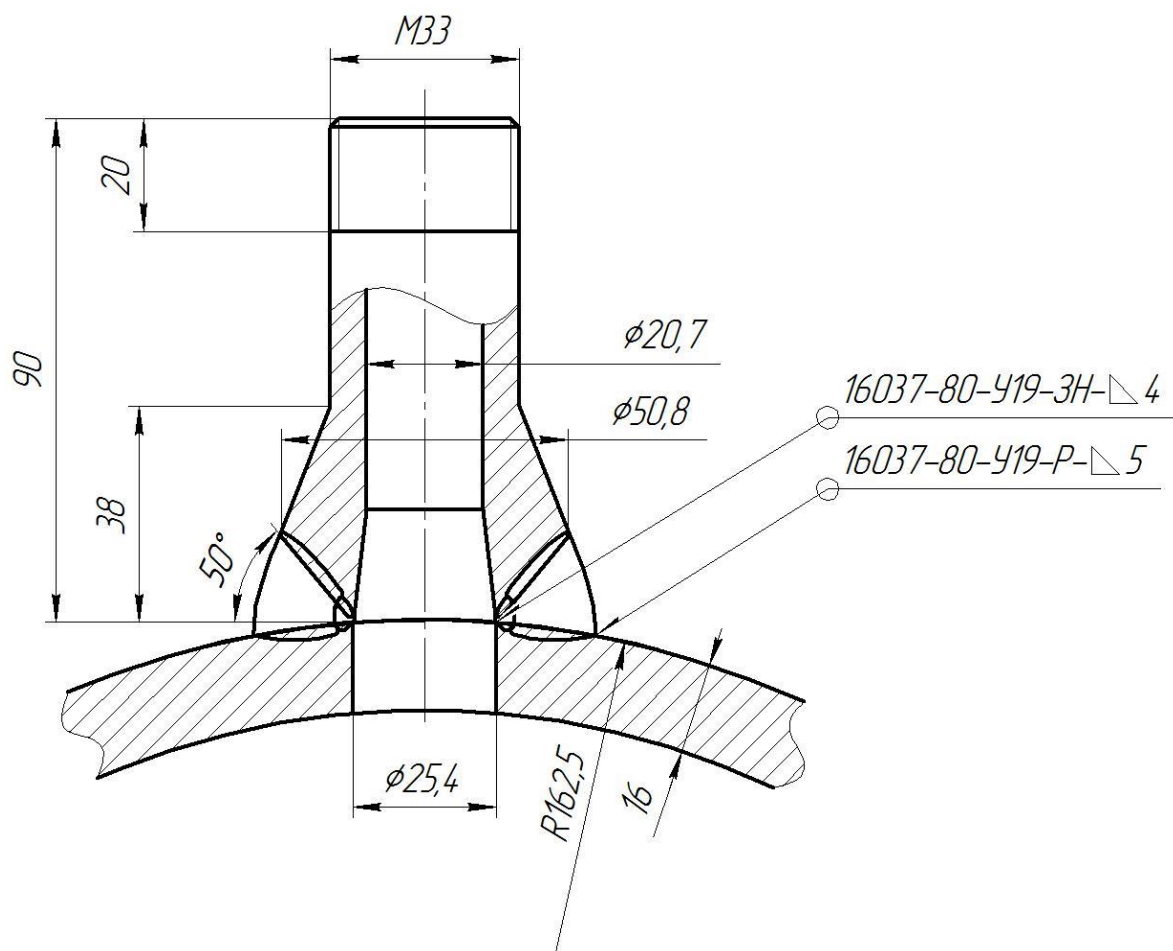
Узел сварки бобышки с трубопроводом.
